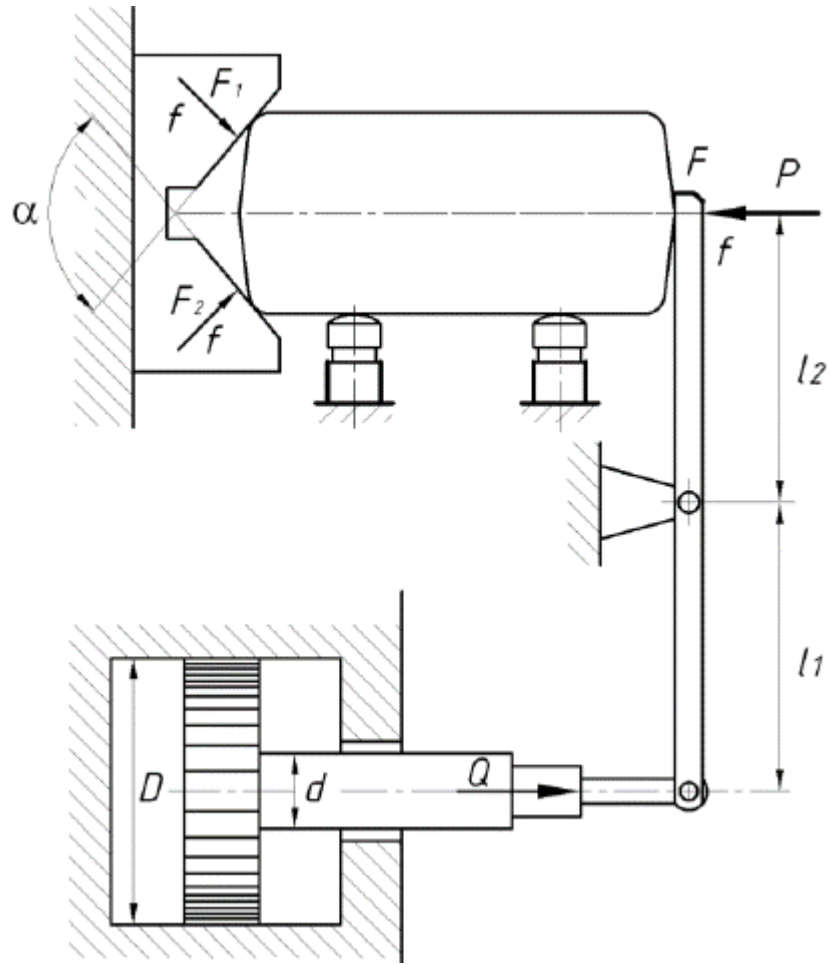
Установка заготовки при фрезерному обробленні
